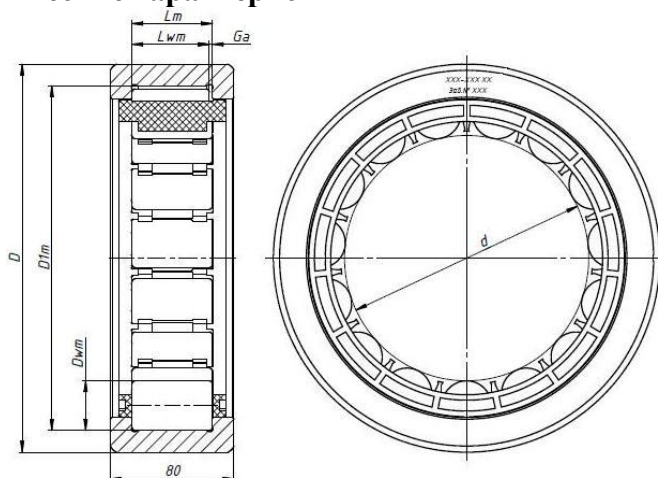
Эскиз мер для поверки приборов модели 4156 с обозначением основных размеров
